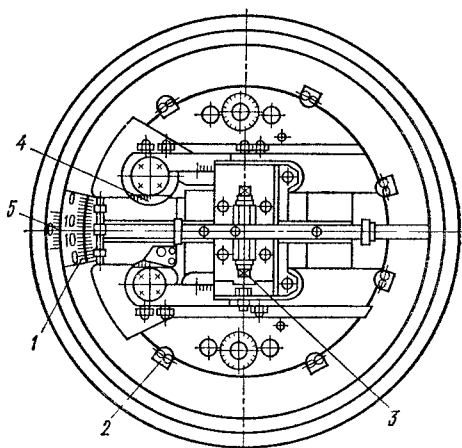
Схема установки суппортов зубострогального станка мод. 5Т23В
